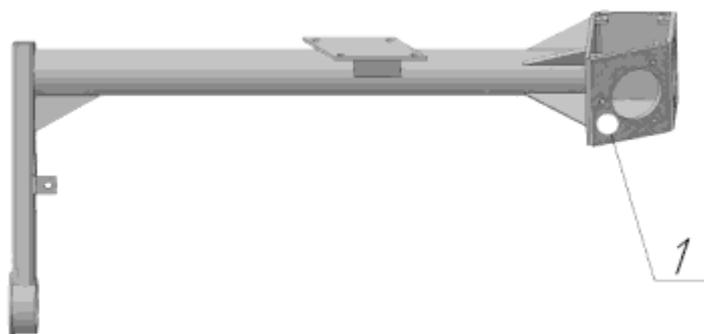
Узел корпуса редуктора УМ ДУ-80/82.02.02
